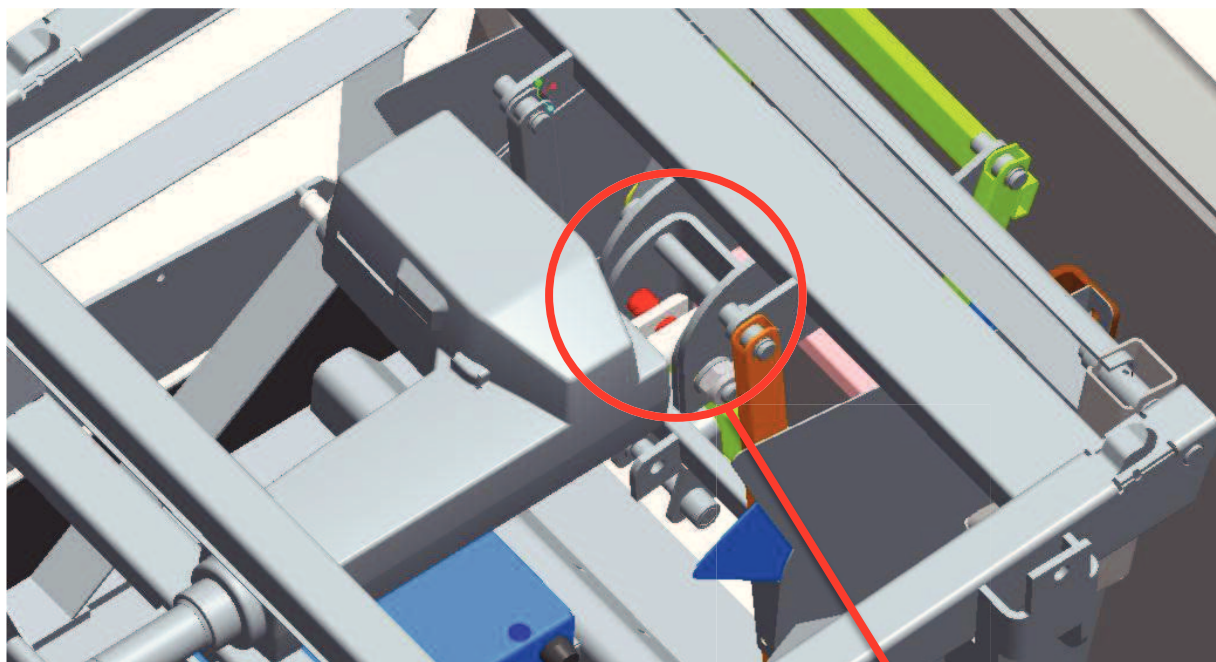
Tvar úchytu motoru Linak LA31 (13)
